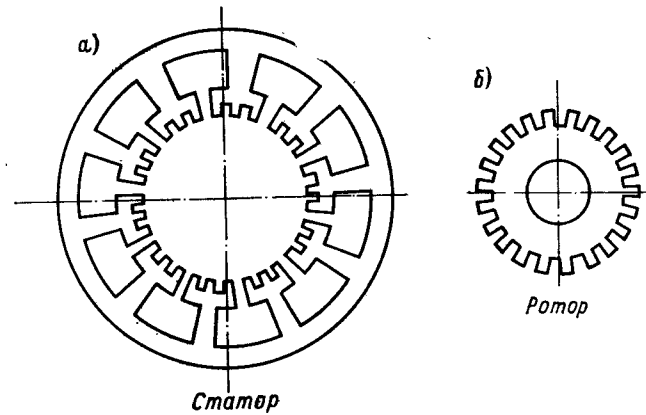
Пластины магнитопровода ноииусного ВТ: а — пластины статора; б — пластины ротора
